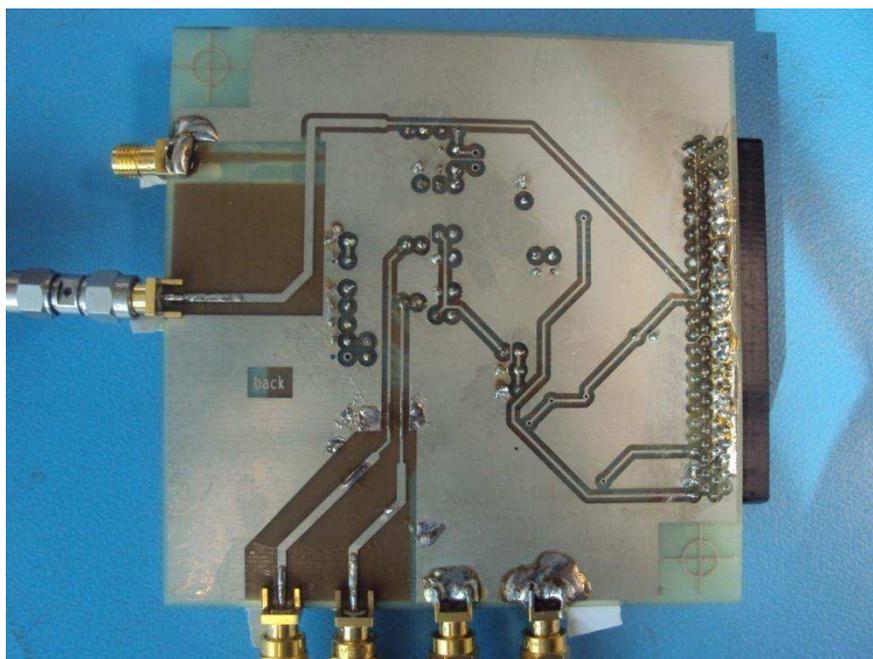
(b) – Circuito impresso desenvolvido com KiCAD, fabricado pela empresa CIRE e soldado no laboratório LCIS (verso).
